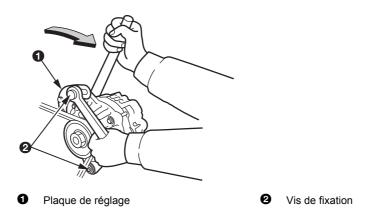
Courroie et sa tension - Inspection et réglage
